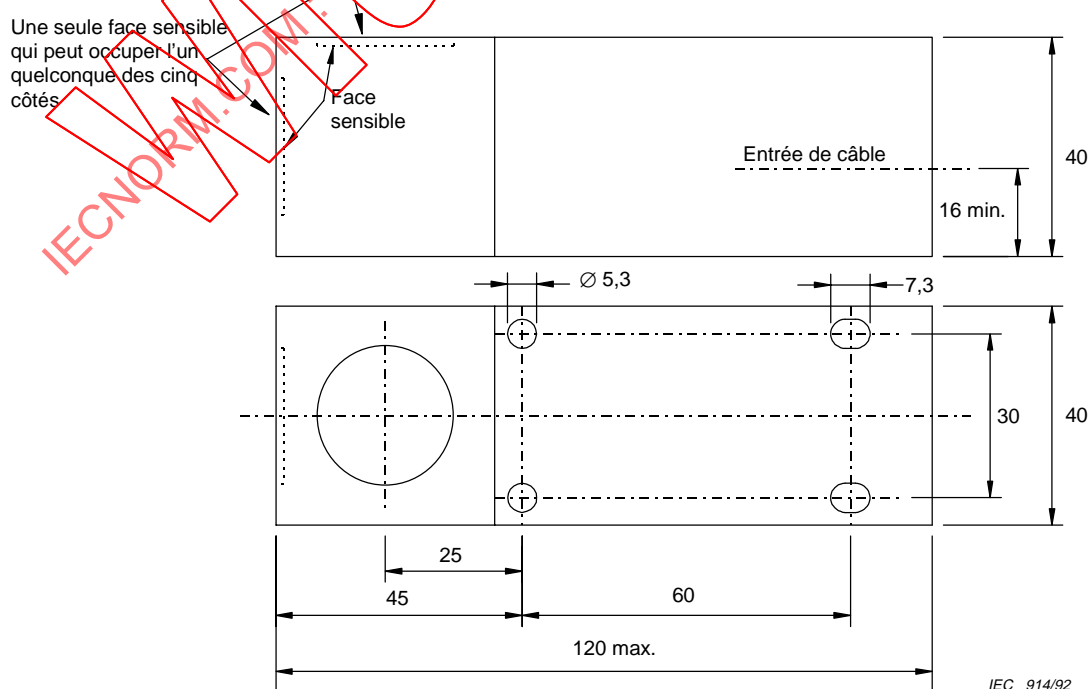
(CC) b – Dimensions, type C40 en millimètres
